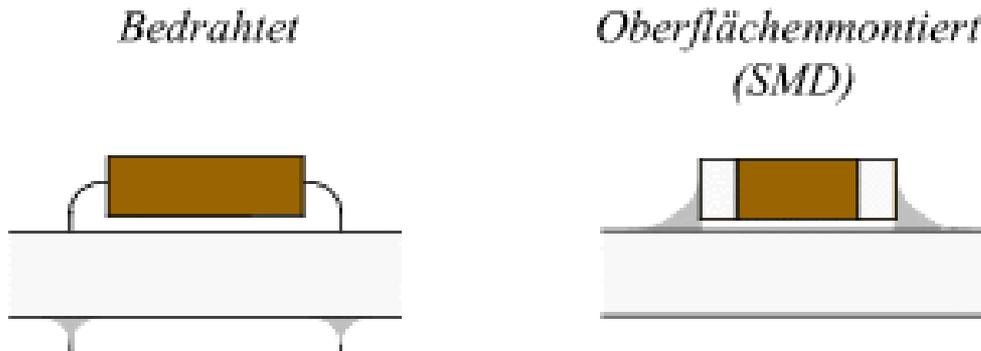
Bedrahtet montiertes und oberflächenmontiertes Bauelement
